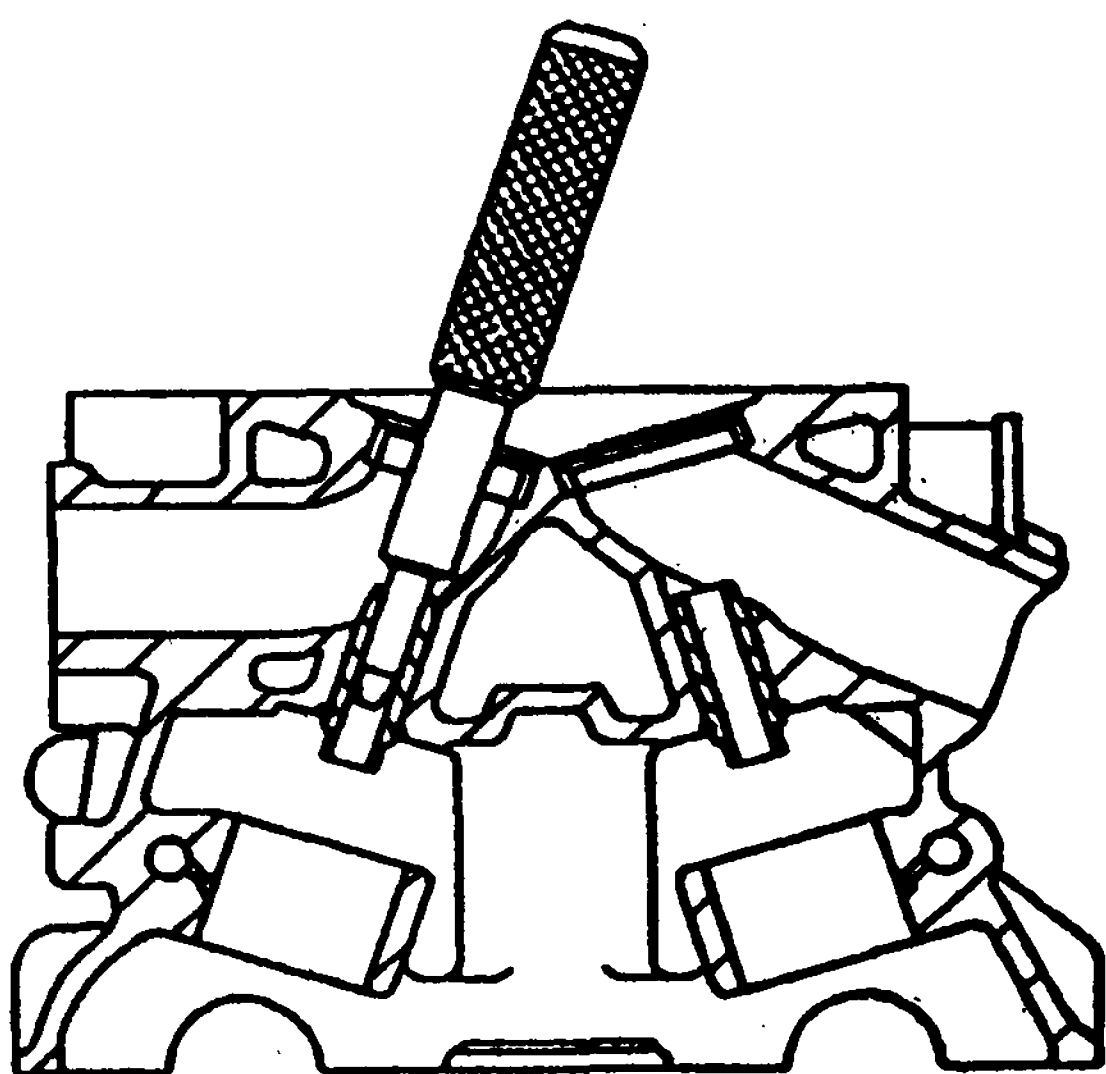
Выпрессовка направляющих втулок клапанов
